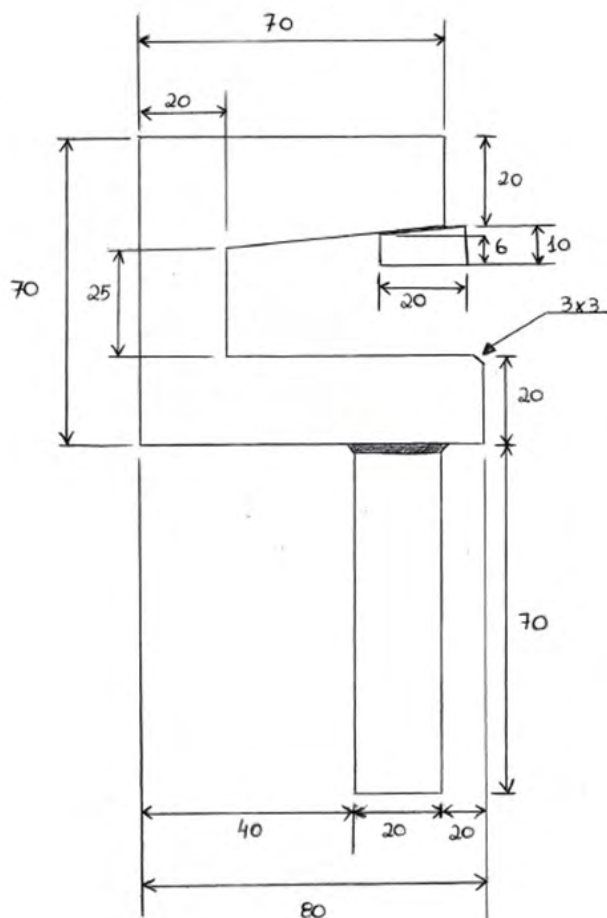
Projeto de detalhamento para fabricação da garra inferior.
